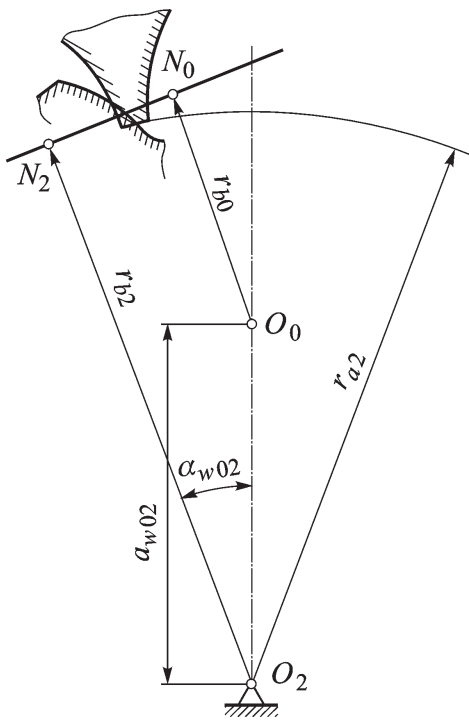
Схема срезания вершины зуба колеса с внутренними зубьями
